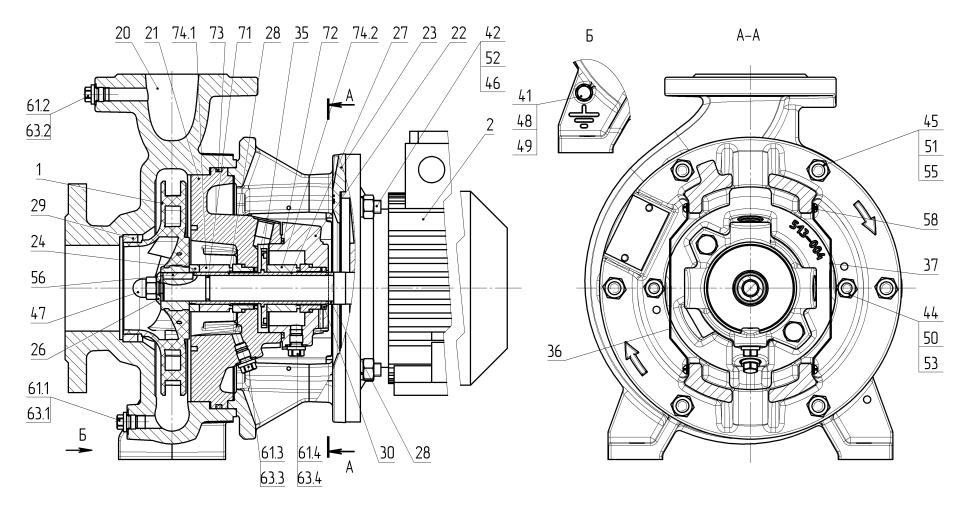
Разрез электронасоса с уплотнением вала 55Т (типоразмеры 40-25-160, 40-32-180, 50-32-200, 80-50-200, 100-80-160, 100-65-200 с hдв ≤ 100)
